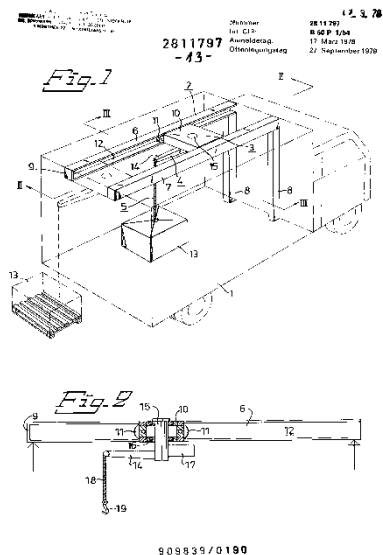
Устройство для погрузки грузов: 2 – несущая рама; 3 – тележка; 4 – стрела; 5 – подъемник
